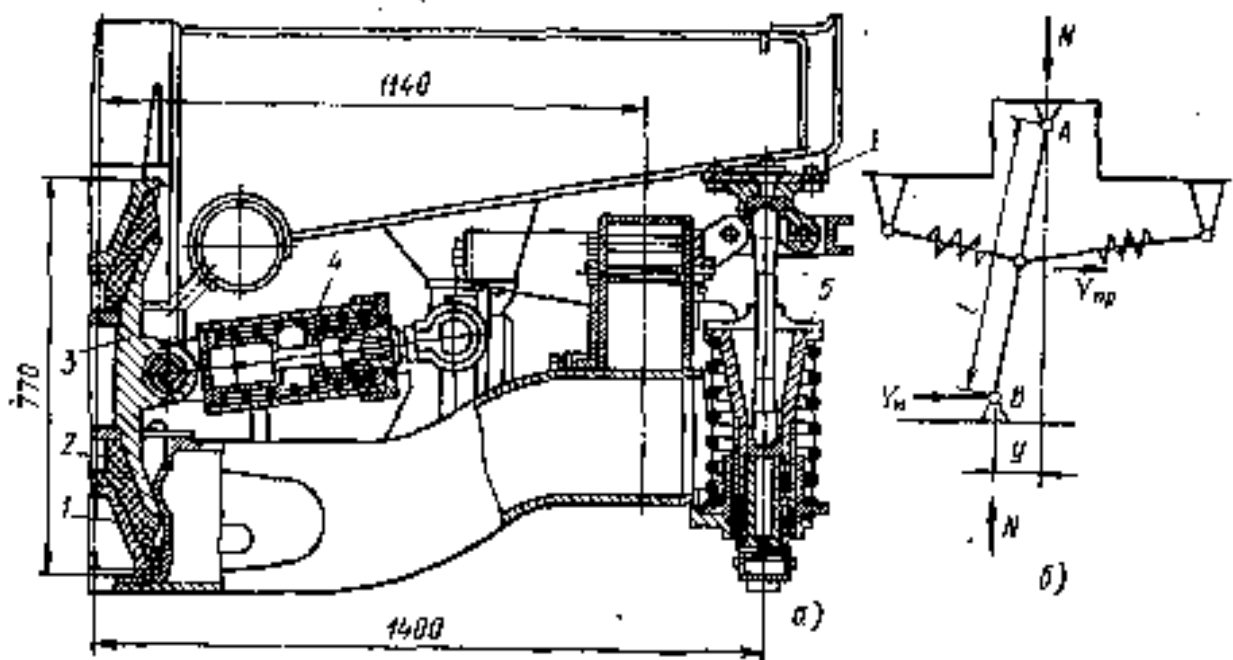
Маятниковий опорно-повертальний пристрій тепловоза ТЕР60:
